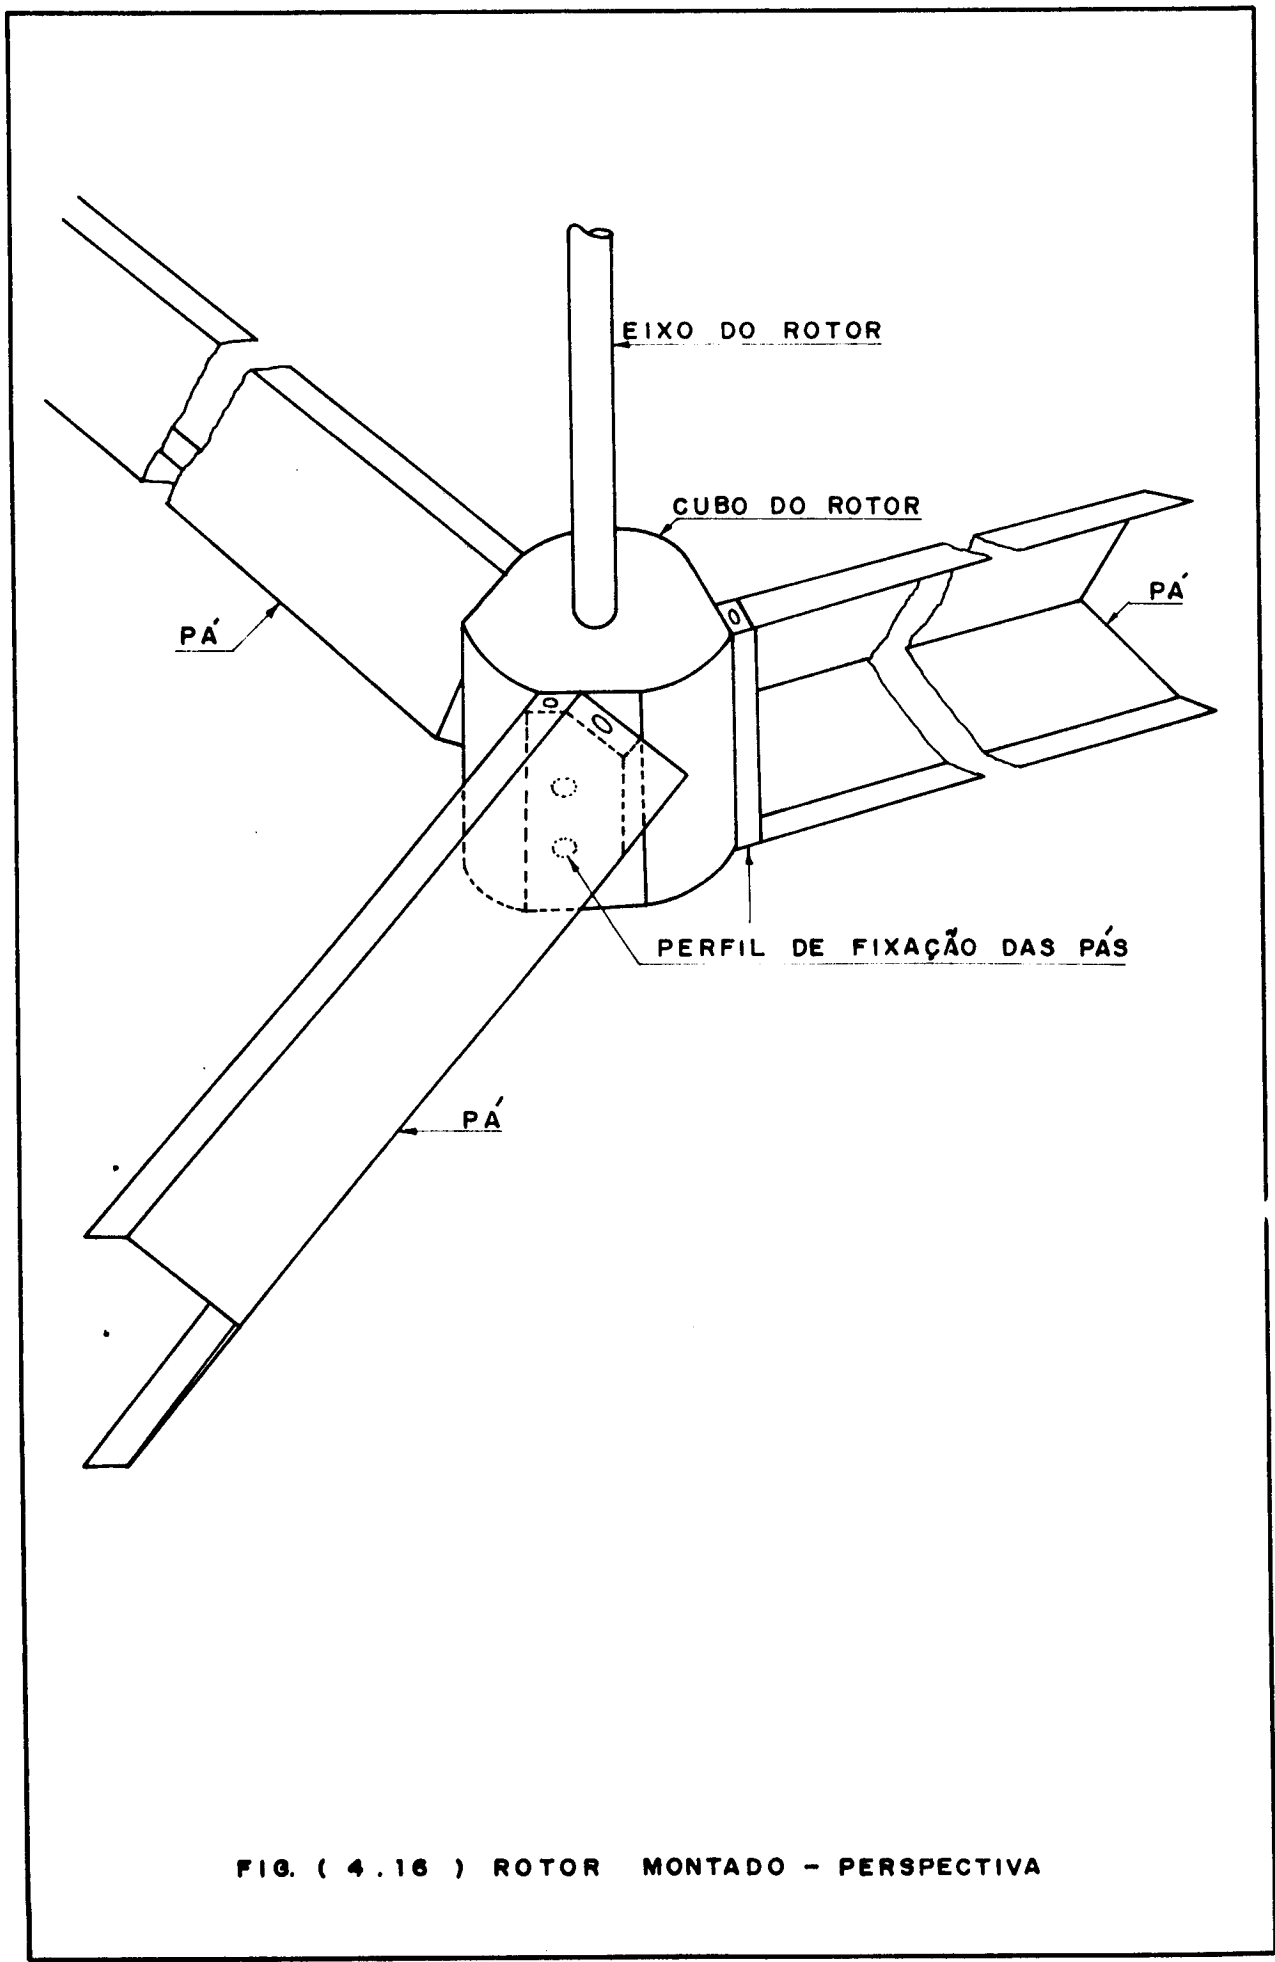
ROTOR MONTADO - PERSPECTIVA
